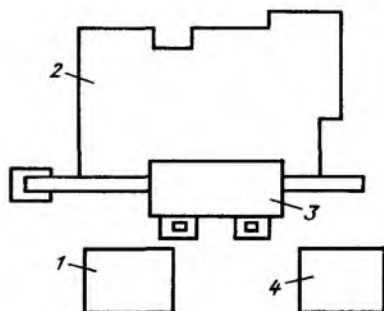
ГПМ на базе токарного станка с ЧПУ:
